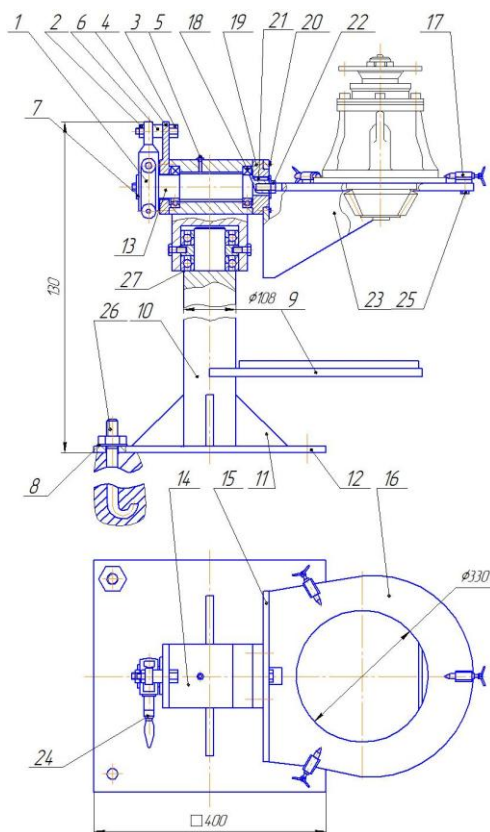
Стенд для обслуживания задних мостов автомобилей: 1- регулировочный рычаг; 2.-гайка; 3 - болт; 4 - задняя крышка; 5 - масленка; 6 - шайба; 7 - шайба; 8 - шайба; 9 - поддон; 10 - стойка; 11 - косынки; 12 -основание; 13 - вал; 14 - корпус; 15 - задняя косынка; 16 - станина; 17 -фиксирующий зажим; 18 - подшипников; 19 - передняя крышка; 20 - болт; 21 - шпонка; 22 - болт; 23 - косынки; 24 - ручка; 25 - болт; 26 - анкерный болт; 27 – упорный подшипник.
